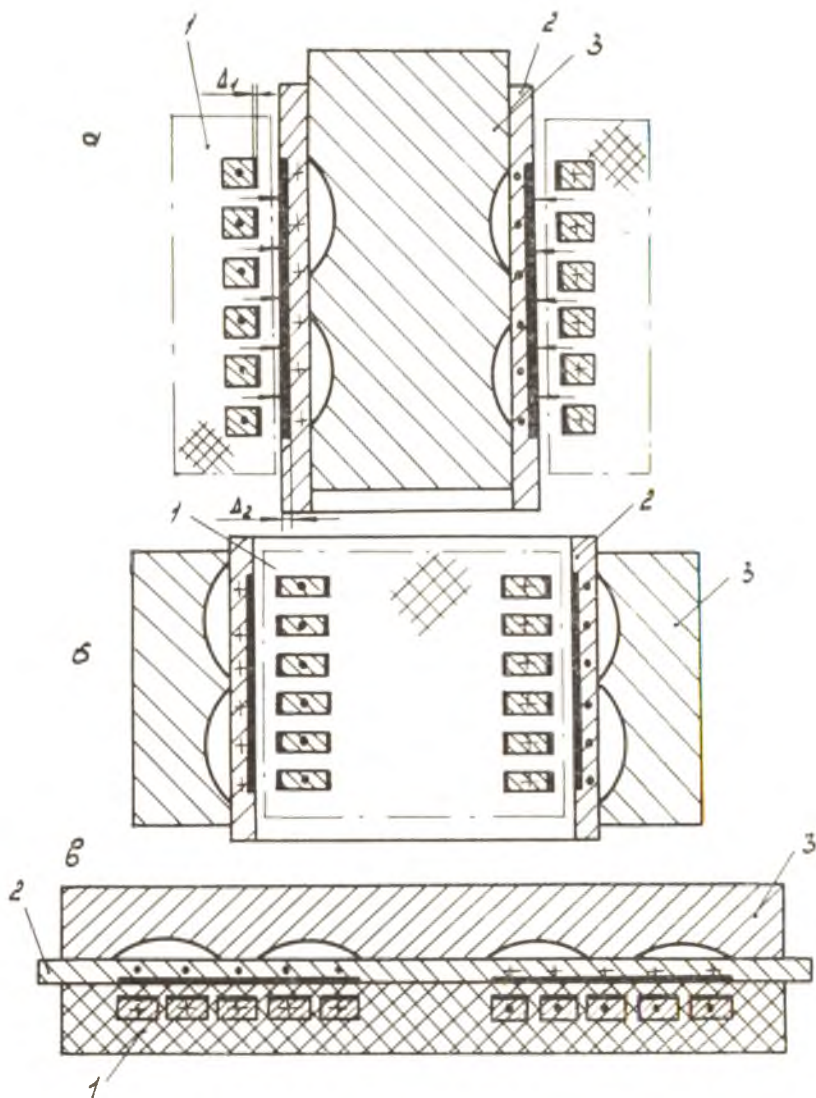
Основные технологические схемы МПОМ: а — обжим трубчатой заготовки, б — раздача трубчатой заготовки, в — штамповка плоской заготовки, 1 — индуктор, 2 — заготовка, 3 — матрица (оправка)
